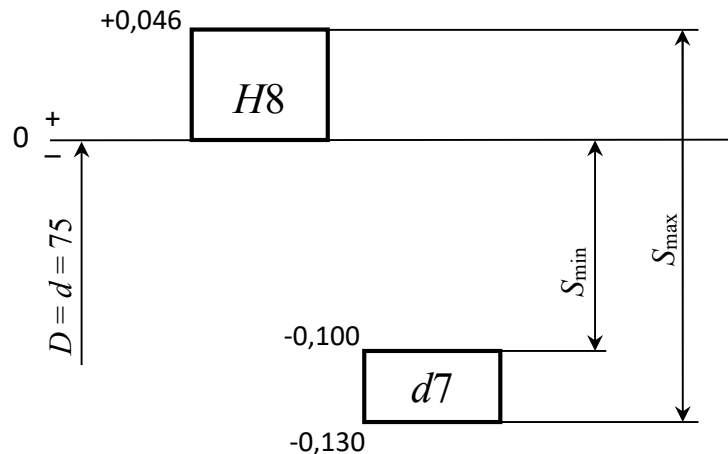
Схема расположения интервалов допусков
